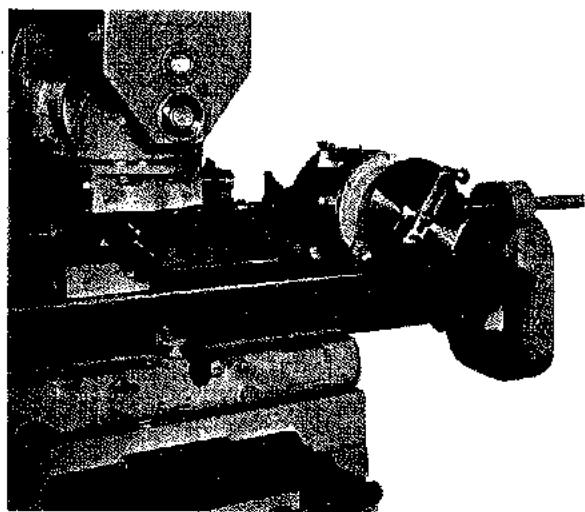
El cabezal universal de fresar en espiral sirve de ayuda en el fresado de un tornillo sin fin (Cincinnati Milling Machine Co.)
